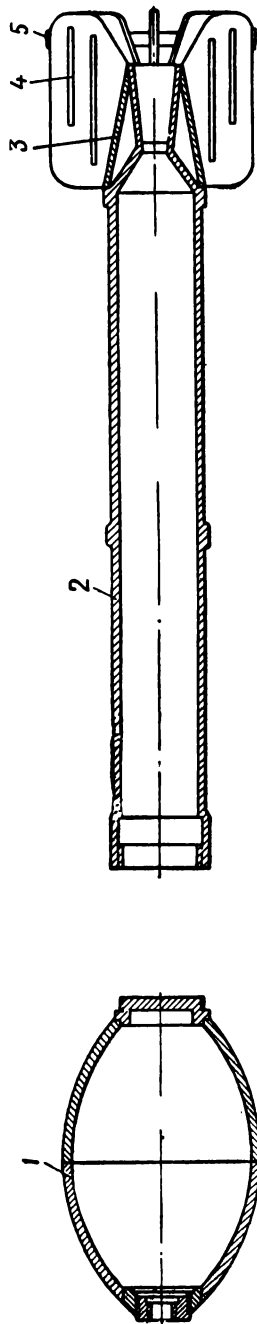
Ракетный снаряд М-31 (СССР), калибр 300 мм, стартовый вес 94,6 кг, максимальная скорость 255 м/сек; 1 — боевая часть (сборка); 2 — ракетная камера (выполняется как одно целое с соплом); 3 — обтекатель; 4 — стабилизатор; 5 — направляющее кольцо стабилизатора
